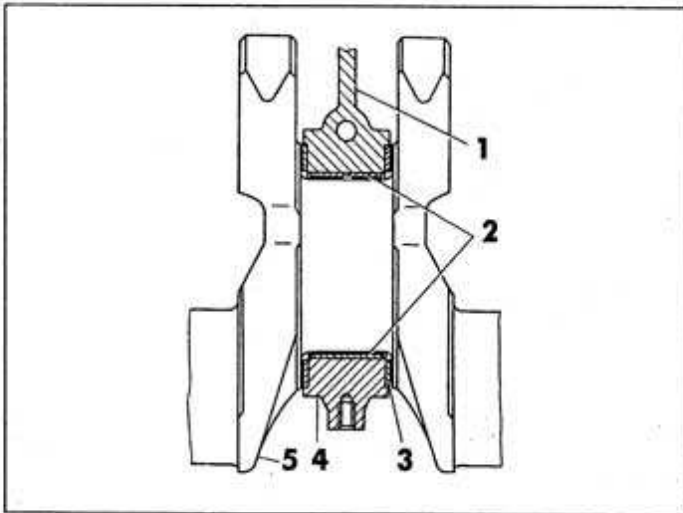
Средний (упорный) подшипник коленчатого вала:
